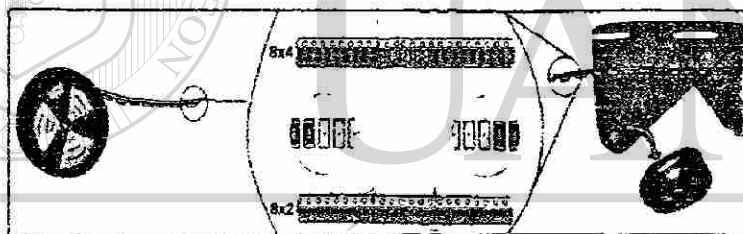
Seccionamiento de los carretes con tijeras antiestáticas.
